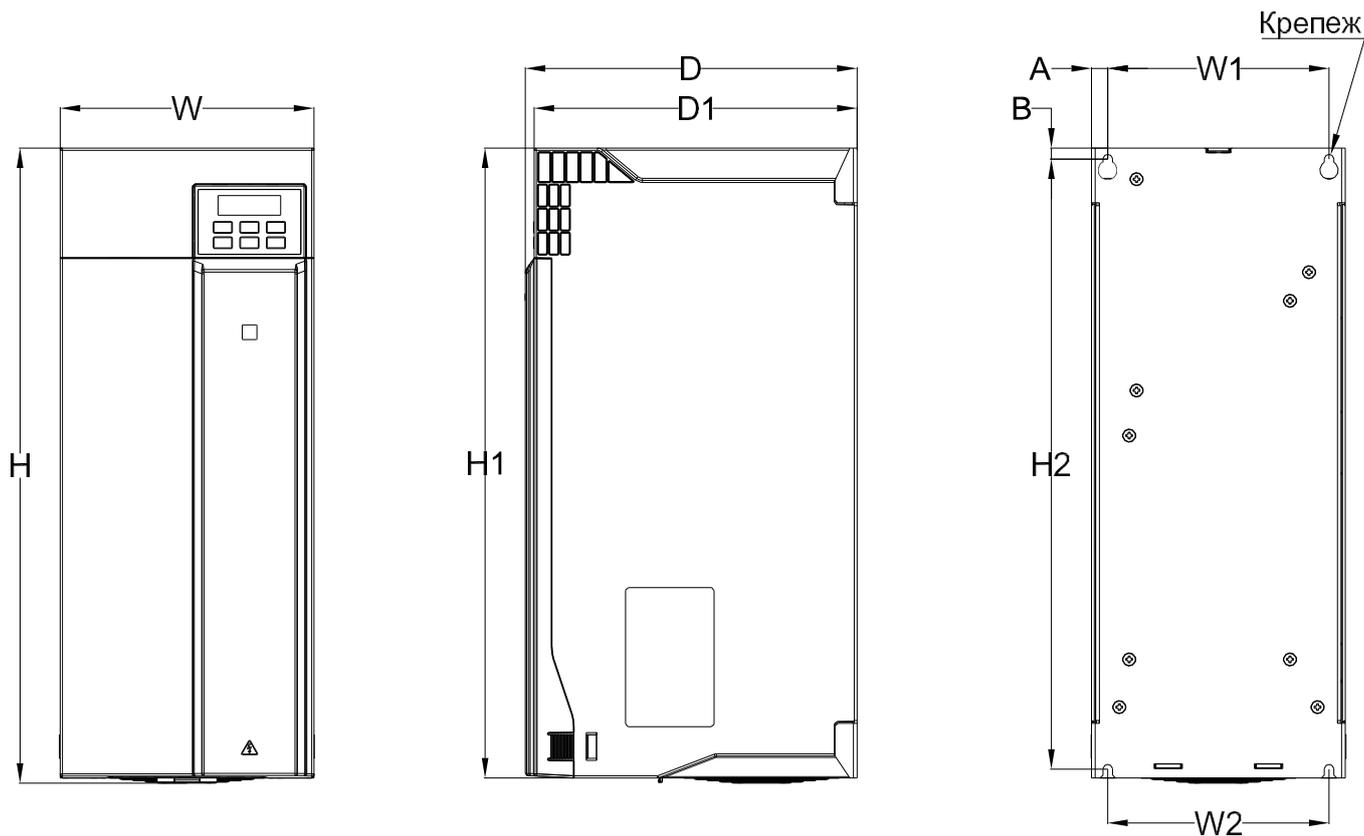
Чертеж преобразователя частоты, типоразмер B5
